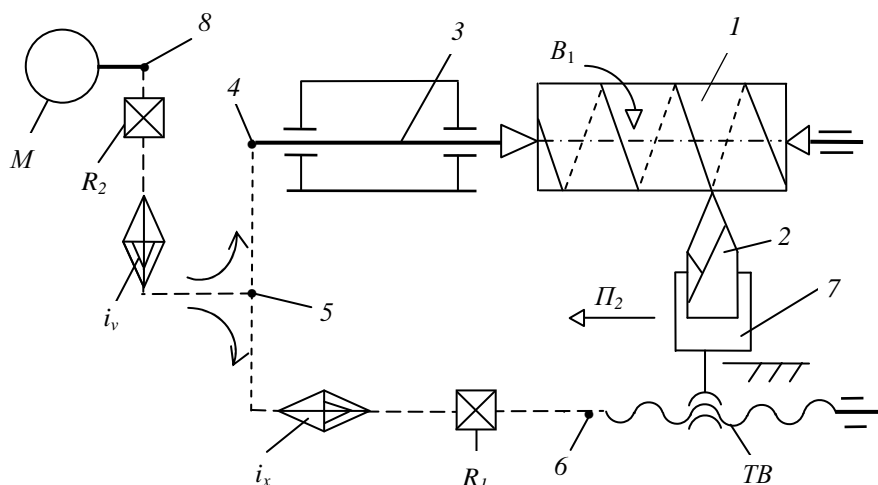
Частная структурная схема станка с механическими связями для нарезания резьбы
